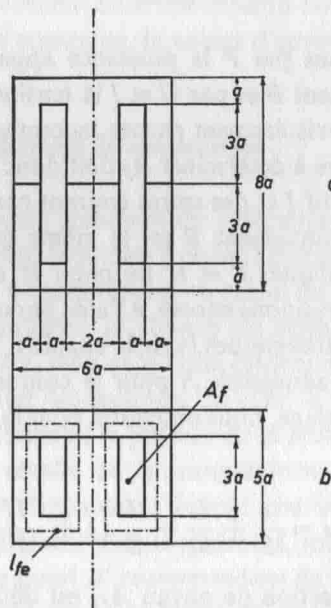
Tôle E-I. De la tôle initiale de dimensions $6a$ et $8a$ (voir la fig. 12a) on découpe deux pièces en forme de E et deux pièces en forme de I, ce qui fournit deux tôles de transformateur. La pièce en I, de dimensions $6a$ et a , fournit la pièce de fermeture pour la pièce en E, de dimensions $4a$ et $6a$ (voir la fig. 12b). Le bras central de la pièce en E, autour duquel se dispose généralement l'enroulement, a une largeur $2a$, la longueur de fer l_{fe} est $12a$, tandis que la section de la fenêtre A_f est égale à $3a^2$.
